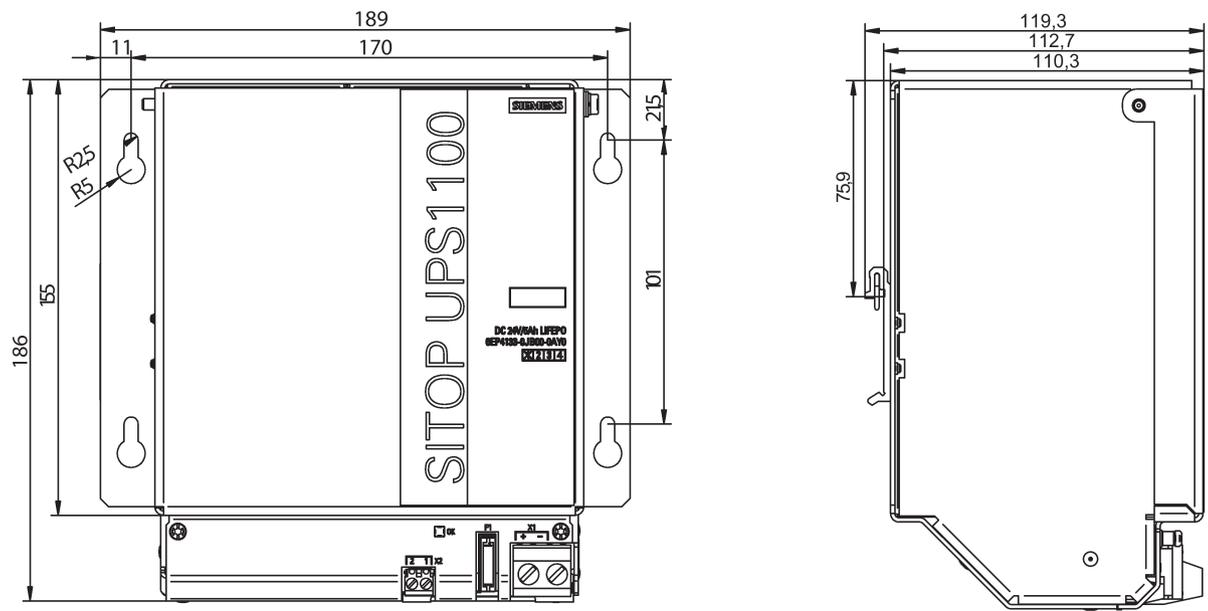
Maßzeichnung 6EP4133-0JB00-0AY0
